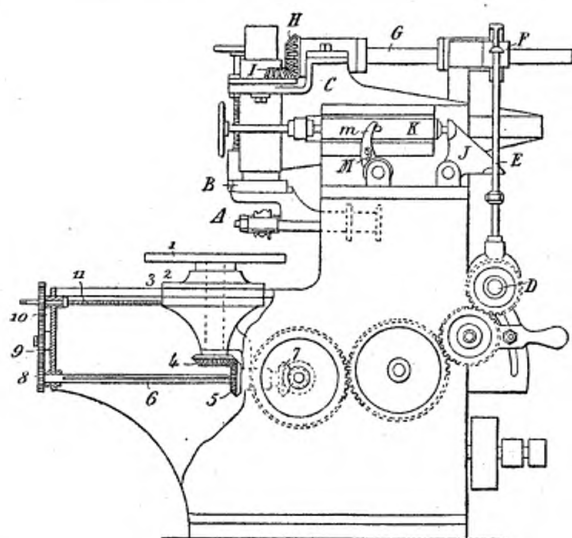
Mécanisme destiné à amener et changer de place la pièce de bois à moulurer.
